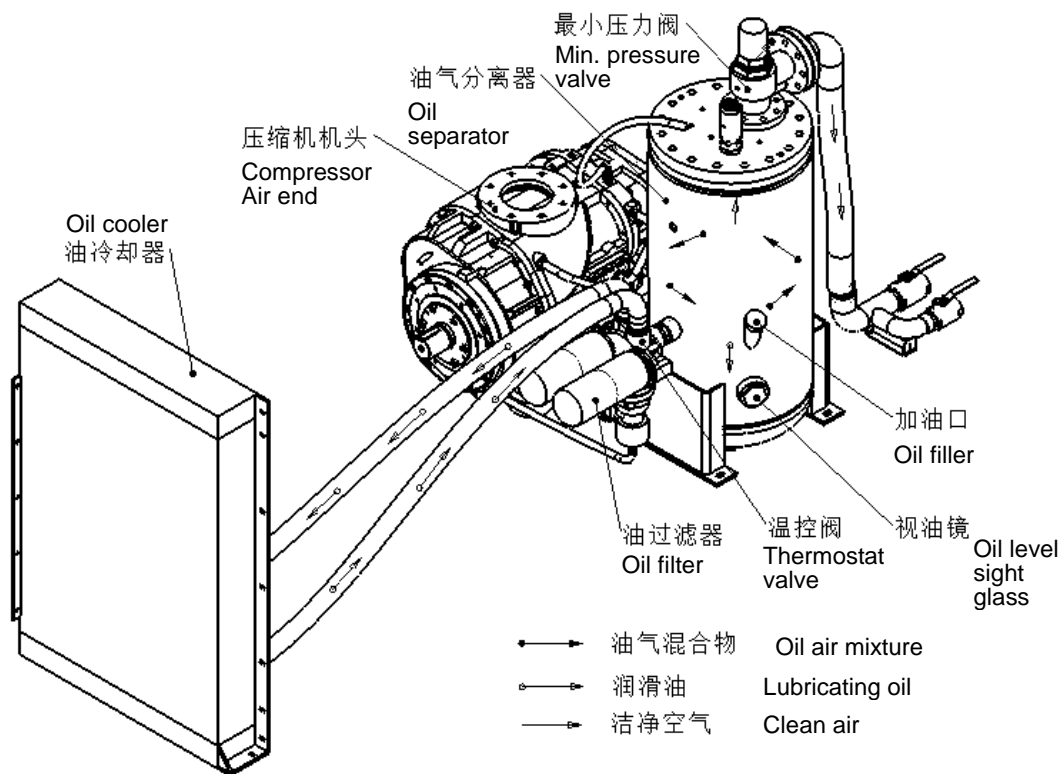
压缩机冷却与润滑系统 Figure 3-2 Compressor Cooling and Lubrication System
